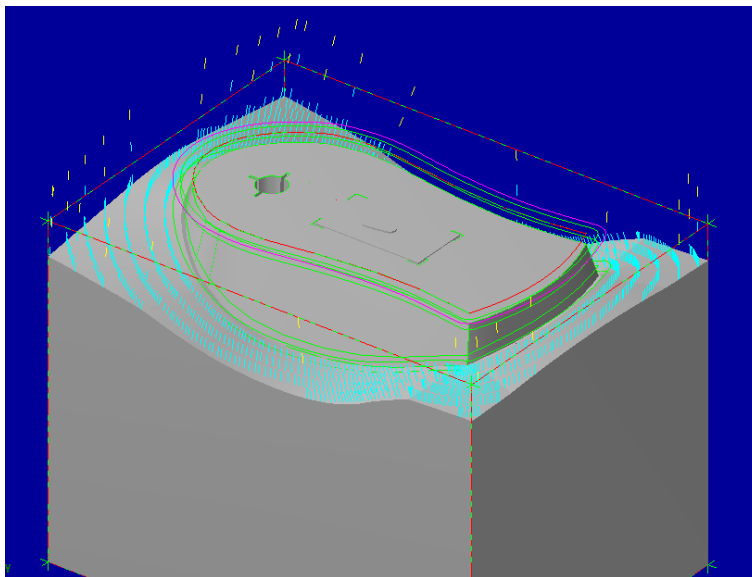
Toolpath da primeira operação de maquinagem do molde do rato.
